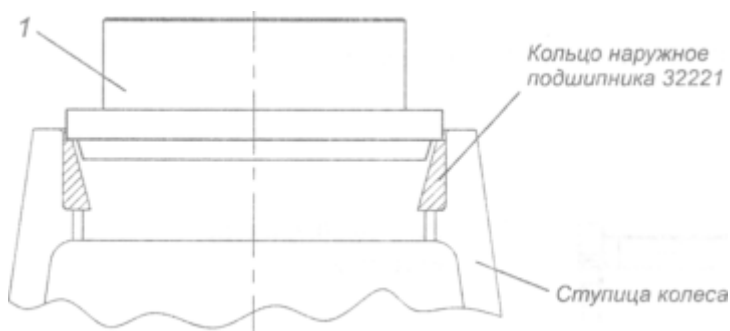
Запрессовка внутреннего кольца подшипника 32221:
